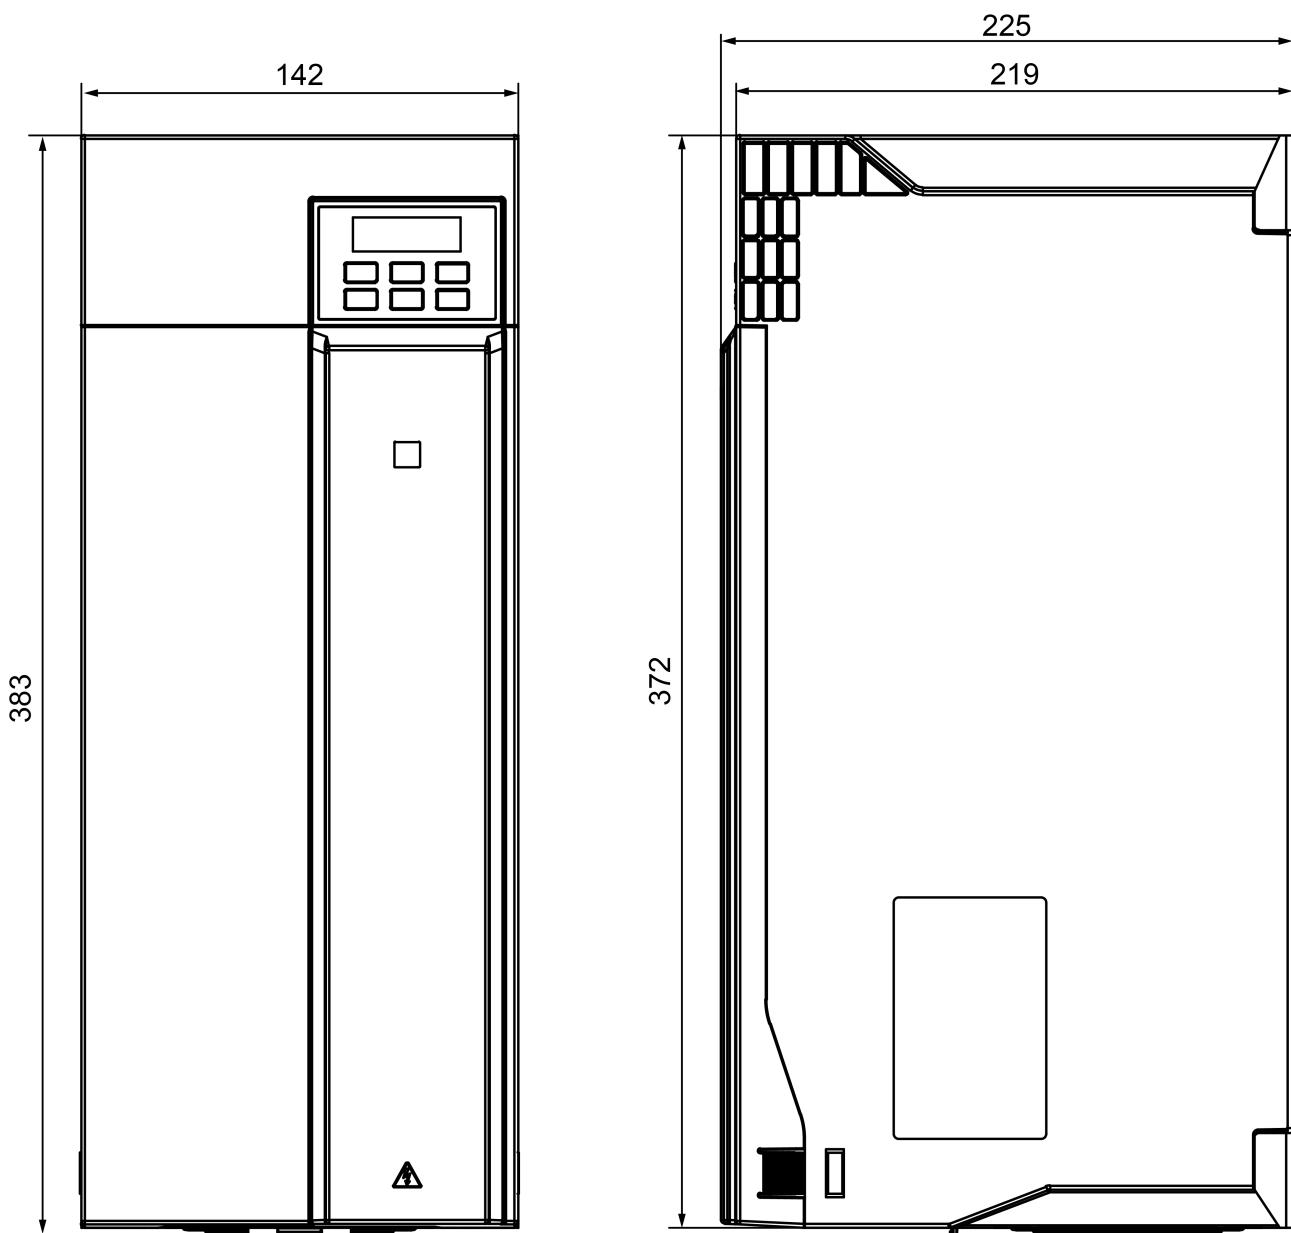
Габаритные размеры прибора в корпусе типоразмера 4
